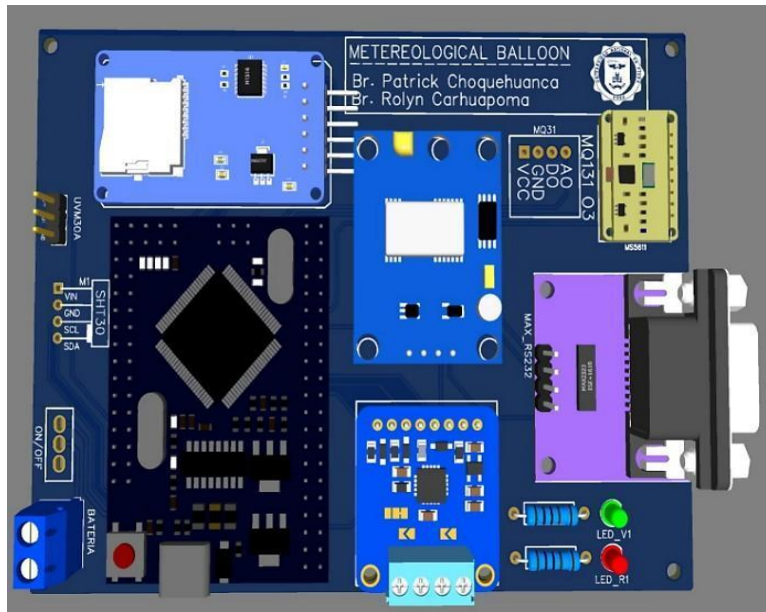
Diseño de la placa PCB con los componentes ensamblados
